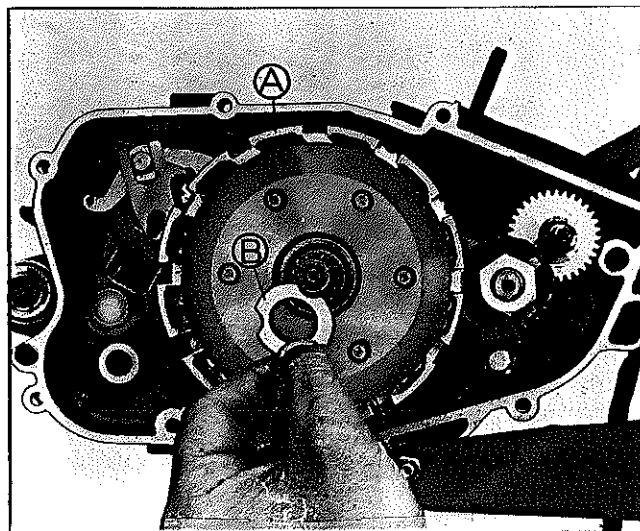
A. CONJUNTO EMBREAGEM CONDUTORA
